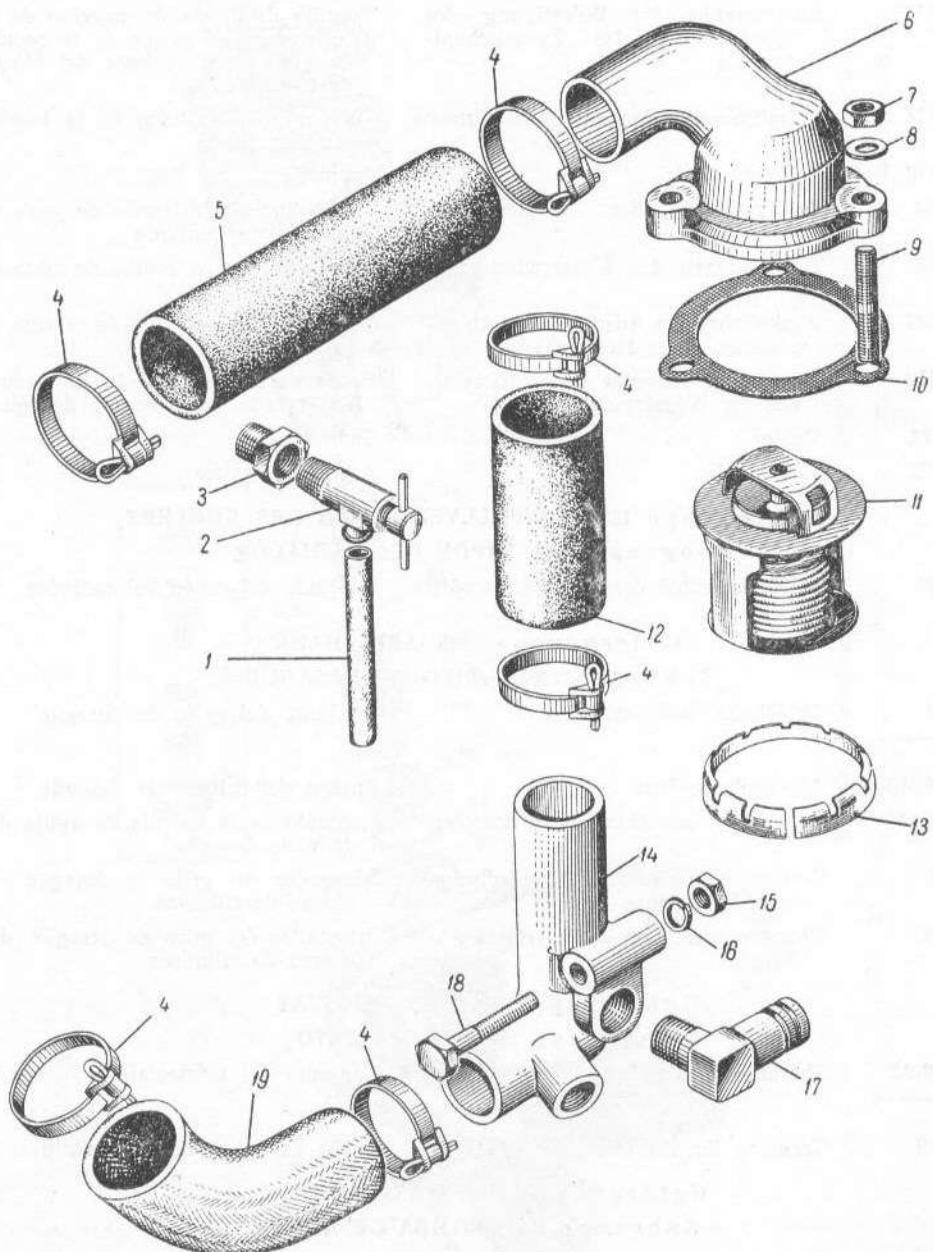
Rohrleitungen, Schläuche und Thermostat der Kühl anlage
